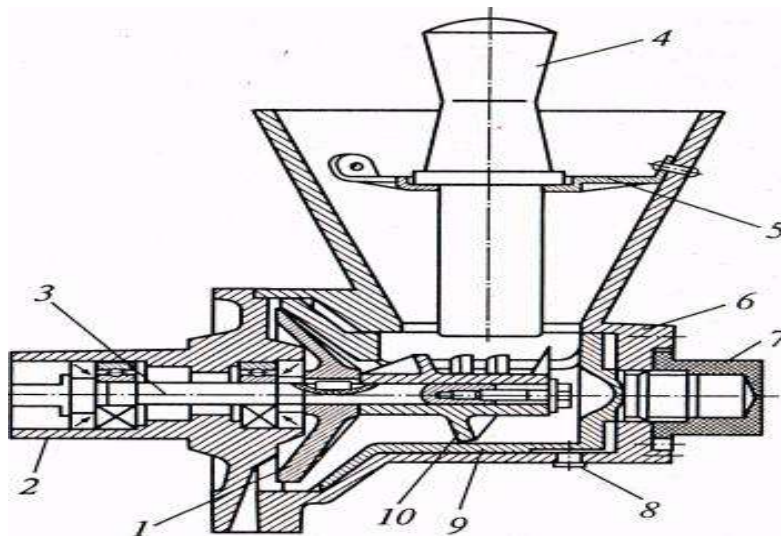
Механізм МИ з конусним робочим органом: 1 – рухоме жорно; 2 – кришка-хвостовик; 3 – вал; 4 – проштовхувач; 5 – запобіжна решітка; 6 – корпус; 7 – регулювальна гайка; 8 – гвинт; 9 – барабан (нерухоме жорно); 10 – шнек
